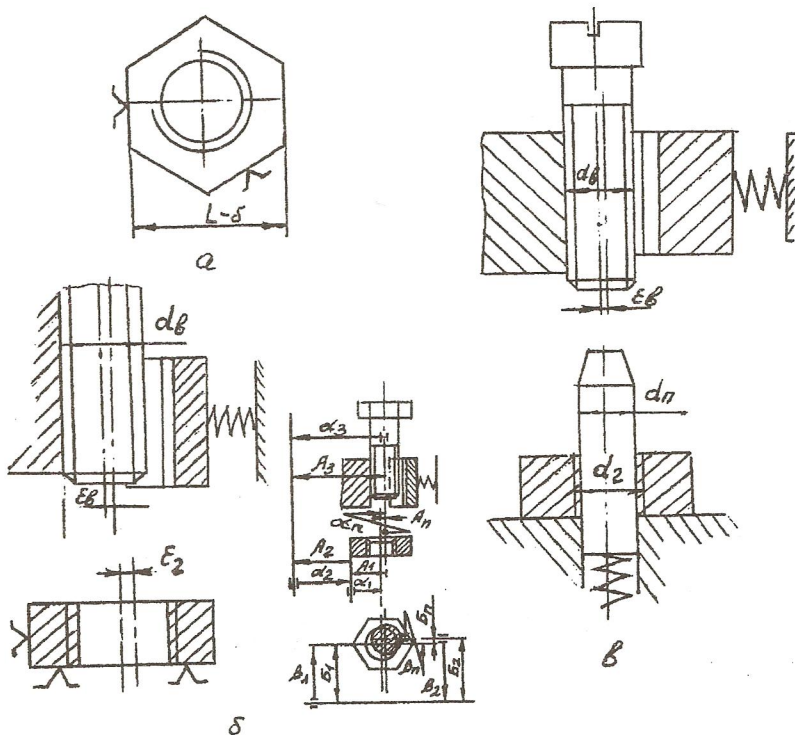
Схемы базирования резьбовых деталей: а - гайки по граням; б - общая схема базирования; в - гайки по внутреннему диаметру резьбы, а винта - по внешнему
